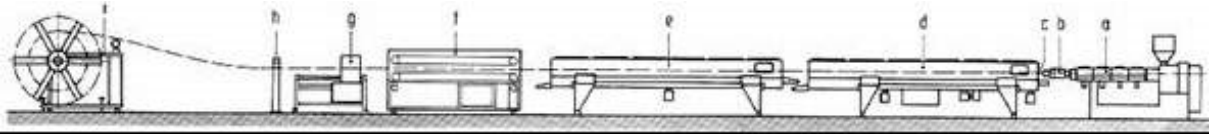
Componentes de una línea de extrusión de tubería flexible: a) extrusora monohusillo, b) cabezal, c) y d) calibración por vacío, e) unidad de enfriado, f), g) y h) recogida y bobinado
